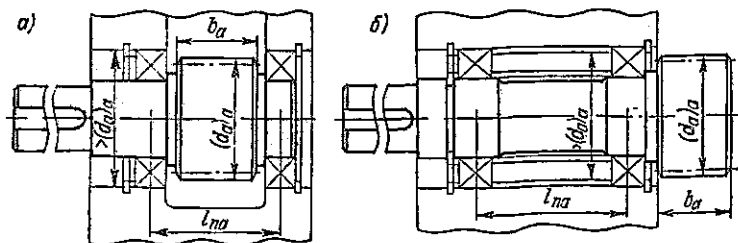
Неплавающие центральные колеса с наружными зубьями
